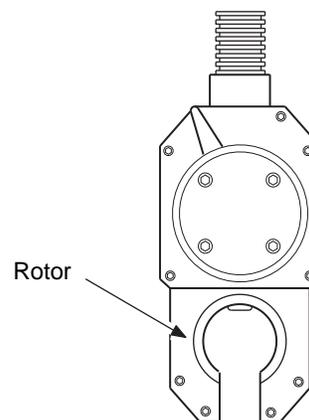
Positionnement de la tête de soudure de façon à voir la rotation du rotor
